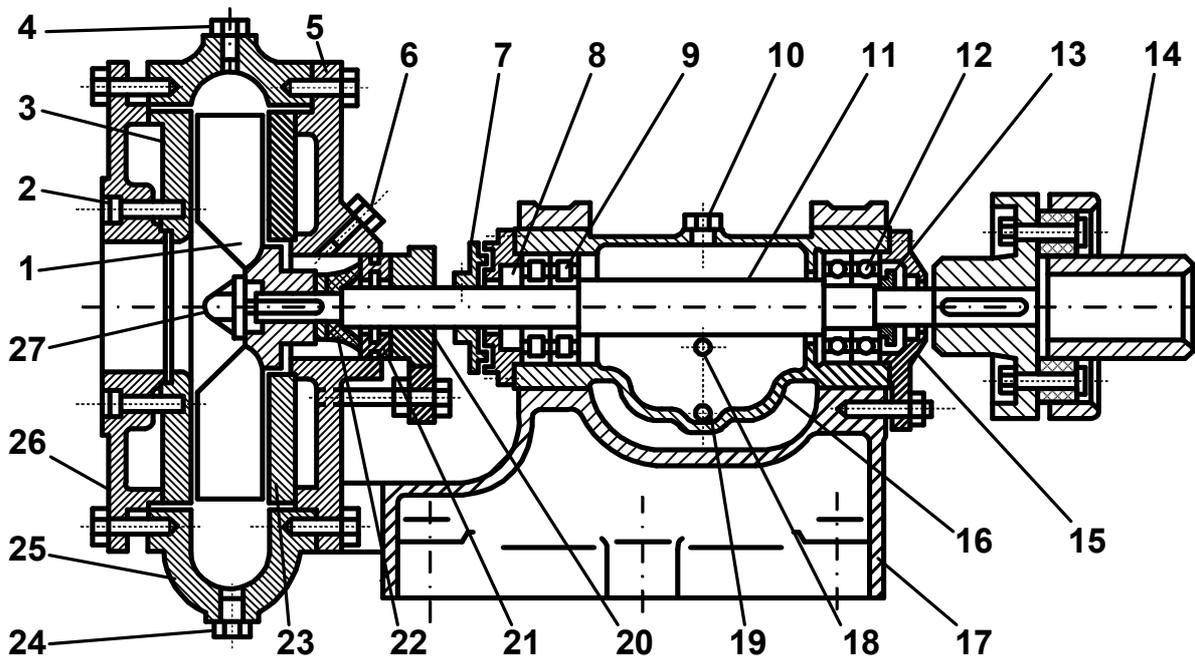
Консольный шламовый насос ШН2-200: 1 – 2-лопаточное открытое рабочее колесо; 2 – крепеж переднего бронедиска; 3 и 23 – передний и задний бронедиски; 4 и 24 – верхняя и нижняя пробки корпуса; 5 и 26 – задняя и передняя крышки корпуса; 6 – подвод для воды; 7 – передний фланец подшипниковой опоры; 8 – манжетное уплотнение подшипников; 9 – передние радиальные подшипники; 10 и 19 – верхняя и нижняя пробки подшипниковой опоры; 11 – вал; 12 – задние радиально-упорные подшипники; 13 – стопорная гайка подшипника; 14 – упругая соединительная муфта; 15 – задний фланец подшипниковой опоры; 16 – корпус подшипниковой опоры; 17 – рама; 18 – отверстие контроля уровня масла; 20 – крышка
